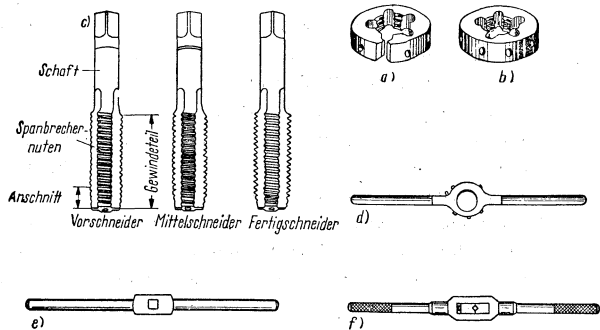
Gewindeschneidwerkzeuge; offenes Schneideisen (a), geschlossenes Schneideisen (b), ein kompletter Satz Gewindebohrer (c), Schneideisenhalter (d), Einlochwindeisen (e) und verstellbares Windeisen (f) für Gewindebohrer
